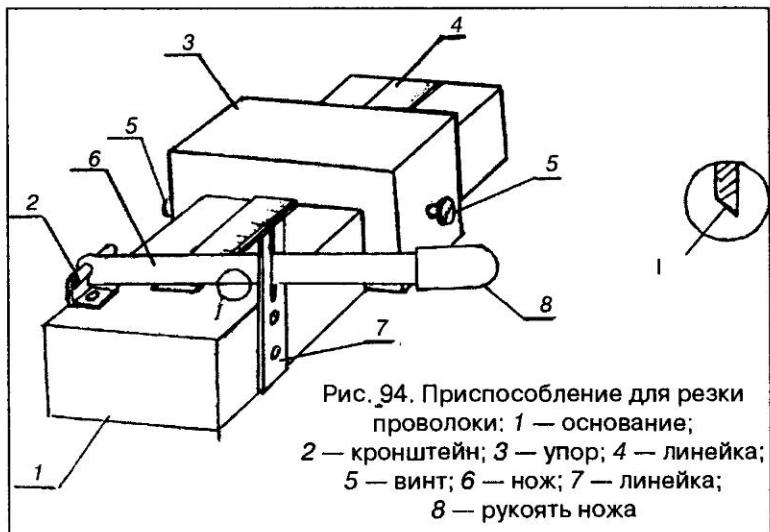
Приспособление для резки проволоки: 1 — основание; 2 — кронштейн; 3 — упор; 4 — линейка; 5 — винт; 6 — нож; 7 — линейка; 8 — рукоять ножа
